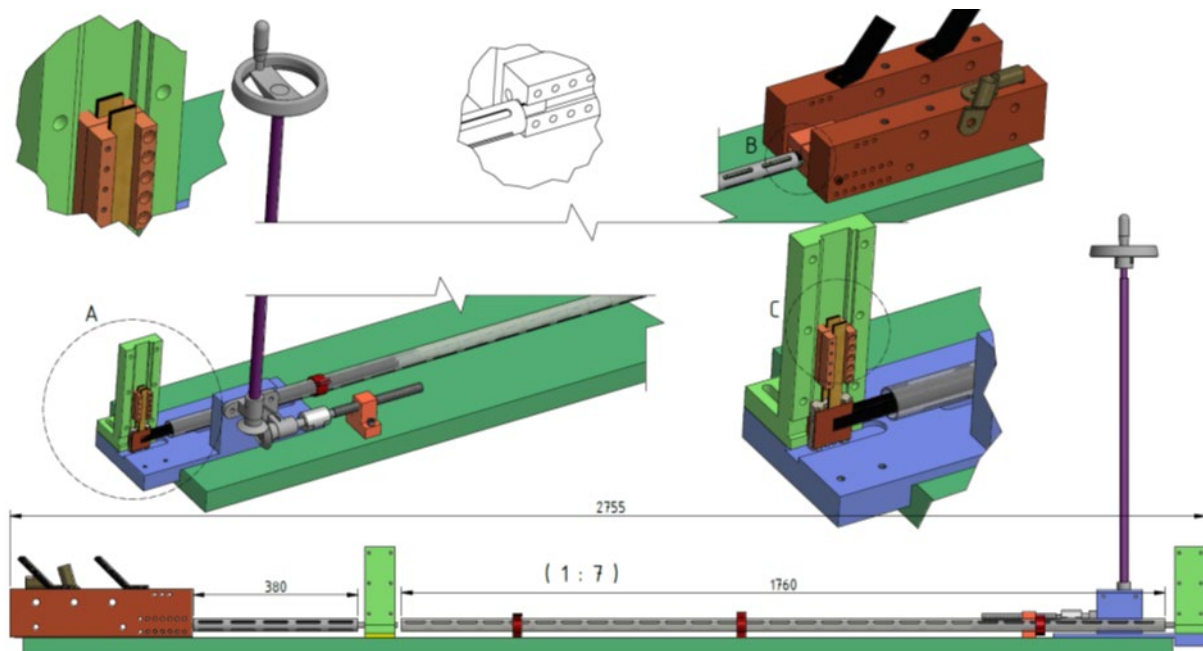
Konstruktionszeichnung des Kabeldemonstrators mit Detailansichten: Detail A: Vorrichtung zur Längenänderung im Kalten; Detail B: Stromeinkopplungskontakte; Detail C: Kurzschlussverbindung zwischen Plus- und Minuspol.
